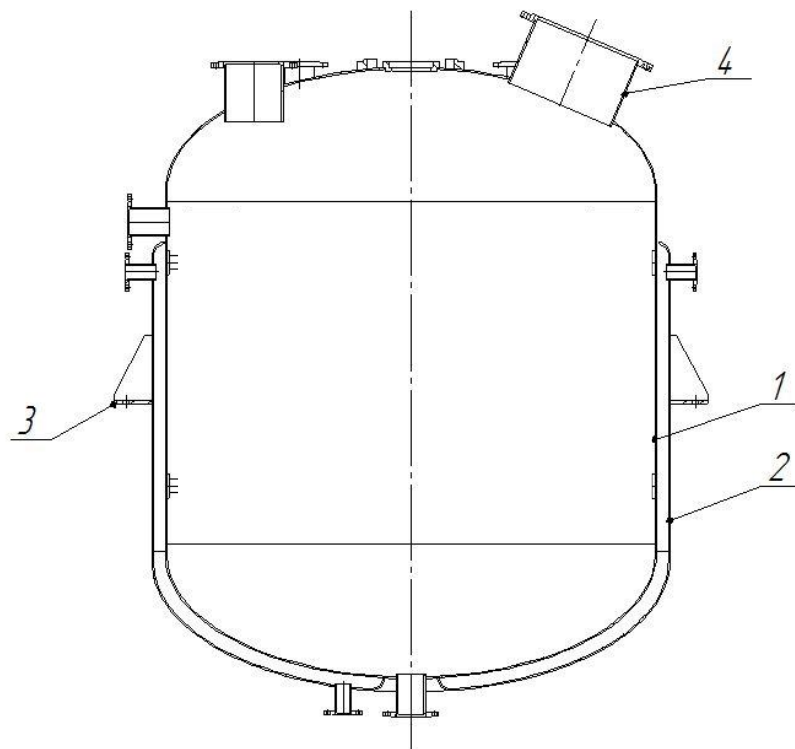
Корпус аппарата: 1-корпус, 2 – рубашка, 3- лапа опорная ,
